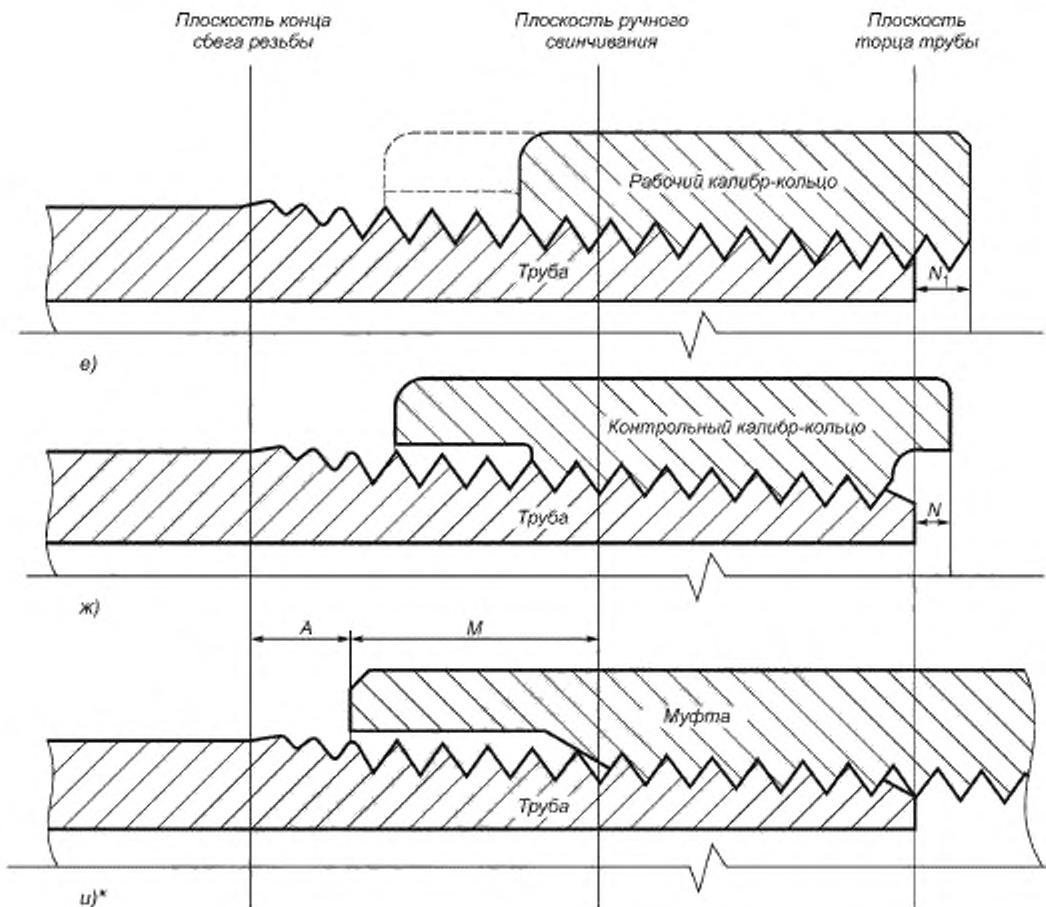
Схема взаимосвязи между контрольными калибрами, рабочими калибрами и резьбой изделий с резьбовыми соединениями LP, SC, LC, NU и EU
